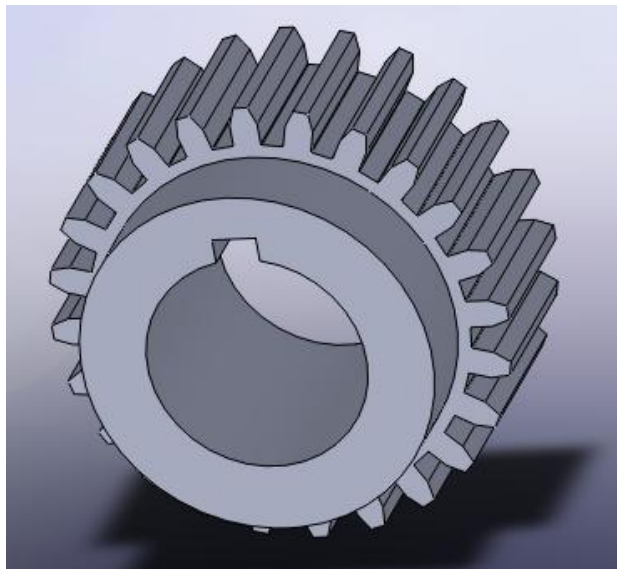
24-зубчаста циліндрична шестерня
